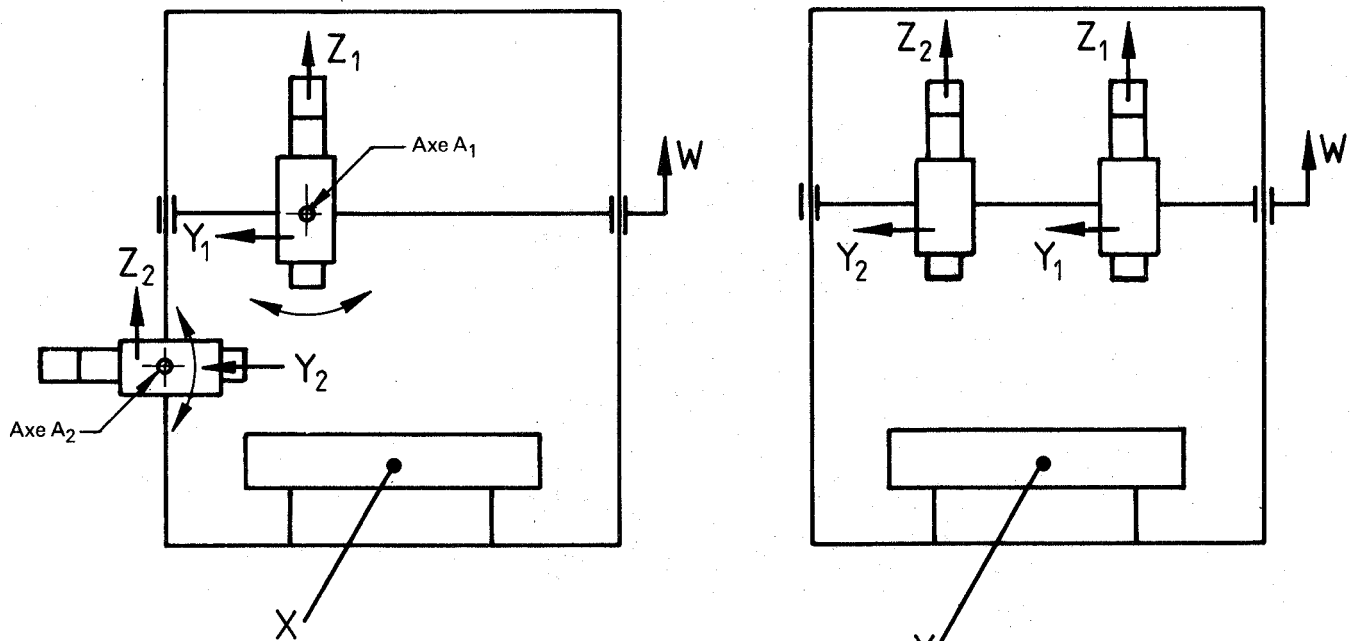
Machine à fraiser à portique fixe à traverse mobile
